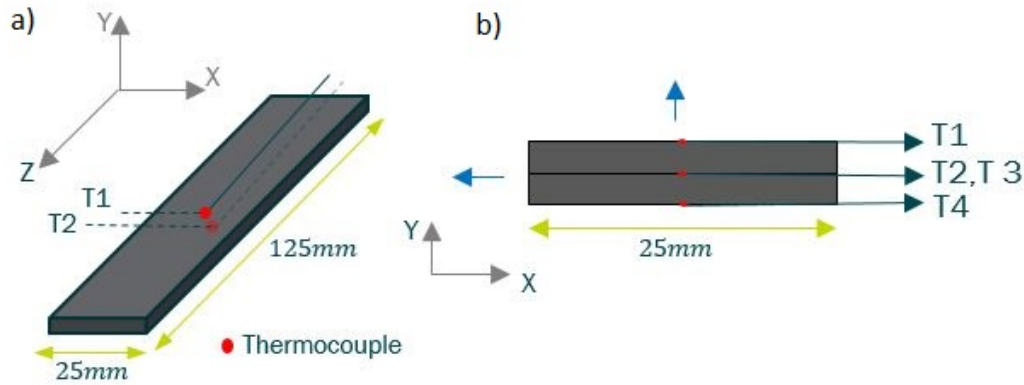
Schématisation des éprouvettes instrumentées :a) vue d'une éprouvette en 3D ; b) vue transversale des deux éprouvettes superposées
